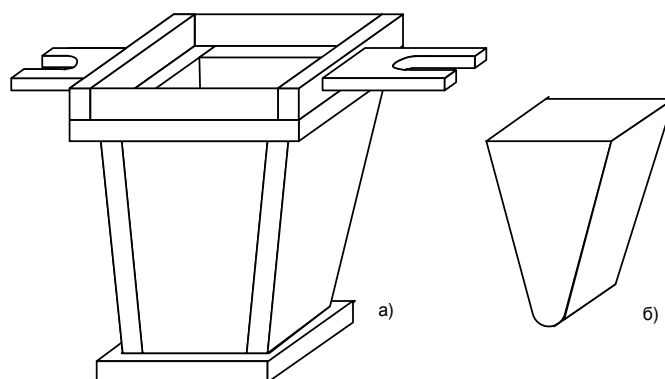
а) кокиль для рабочей части; б) отливка рабочей части
